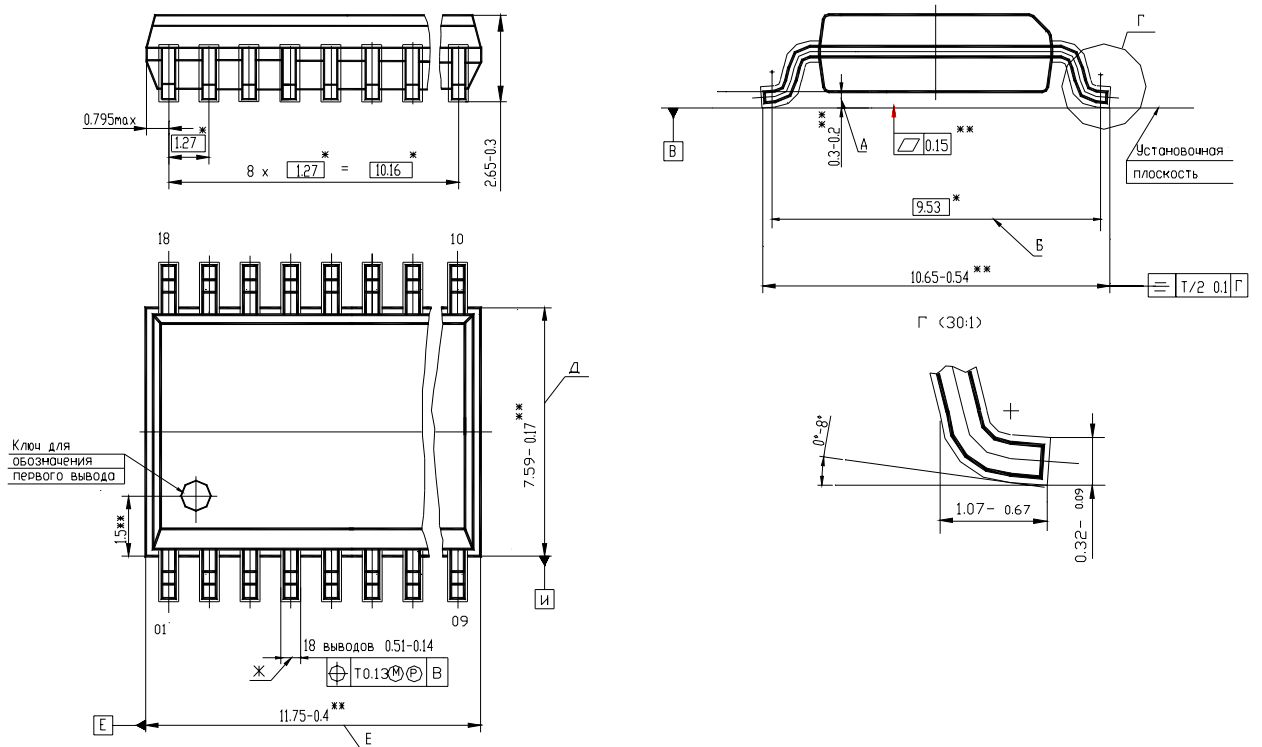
Габаритный чертеж корпуса MS-013AB
